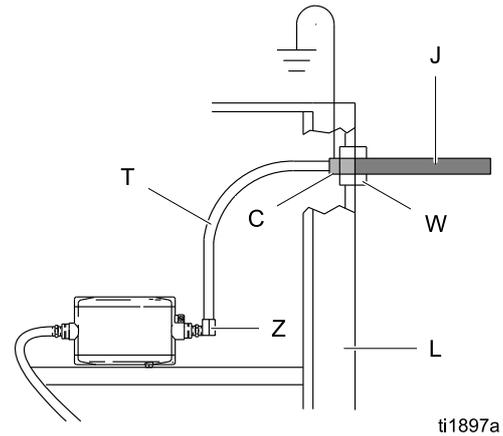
Anschlüsse am WB100-Gehäuse für abgeschirmten Schlauch 24M732
